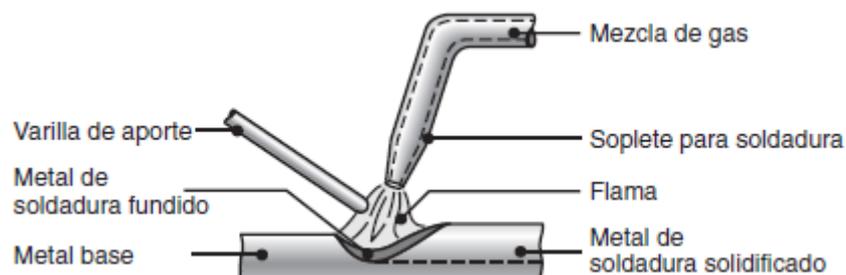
Principio de operación de la soldadura de oxígeno y combustibles gaseosos
